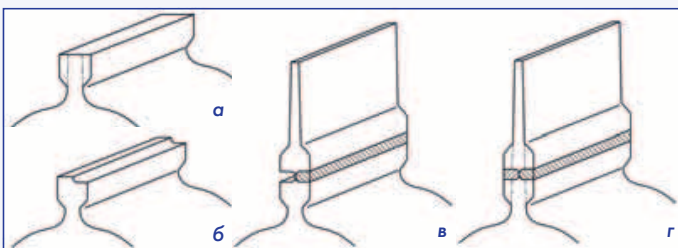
Способ ремонта монокоилс с использованием лазерной сварки: а) привулочная часть диска; б) выполнение углублений; в) заполнение углублений; г) подготовленный к сварке стык
